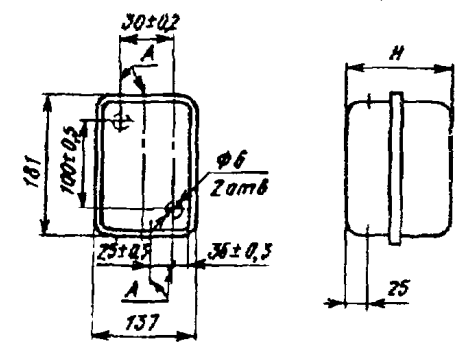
Габаритные, установочные размеры пускателей типа ПМ12-010 реверсивных в оболочках степени защиты IP40
